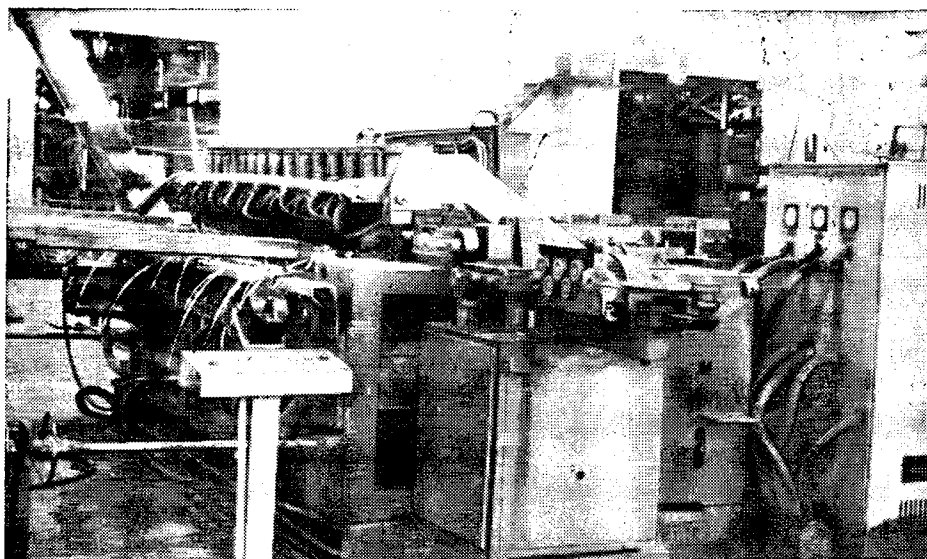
Установка поперечной подачи арматурной стали в электродную зону сварочной машины
